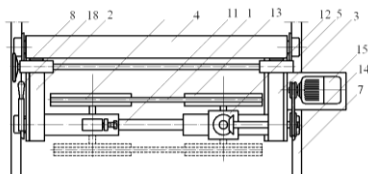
Общий вид ленточнопильного станка (вид сверху)
